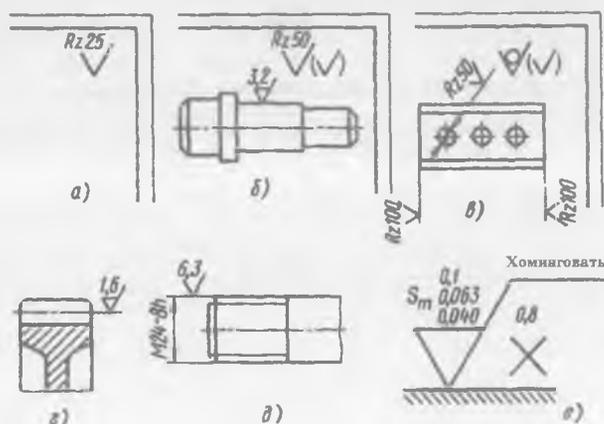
Обозначение шероховатости поверхности (по O`z DSt 646-95).
